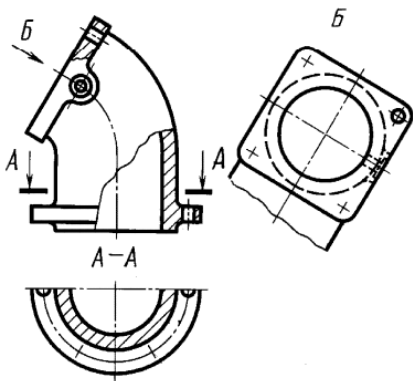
Дополнительный вид, обозначенный на чертеже (Б)
